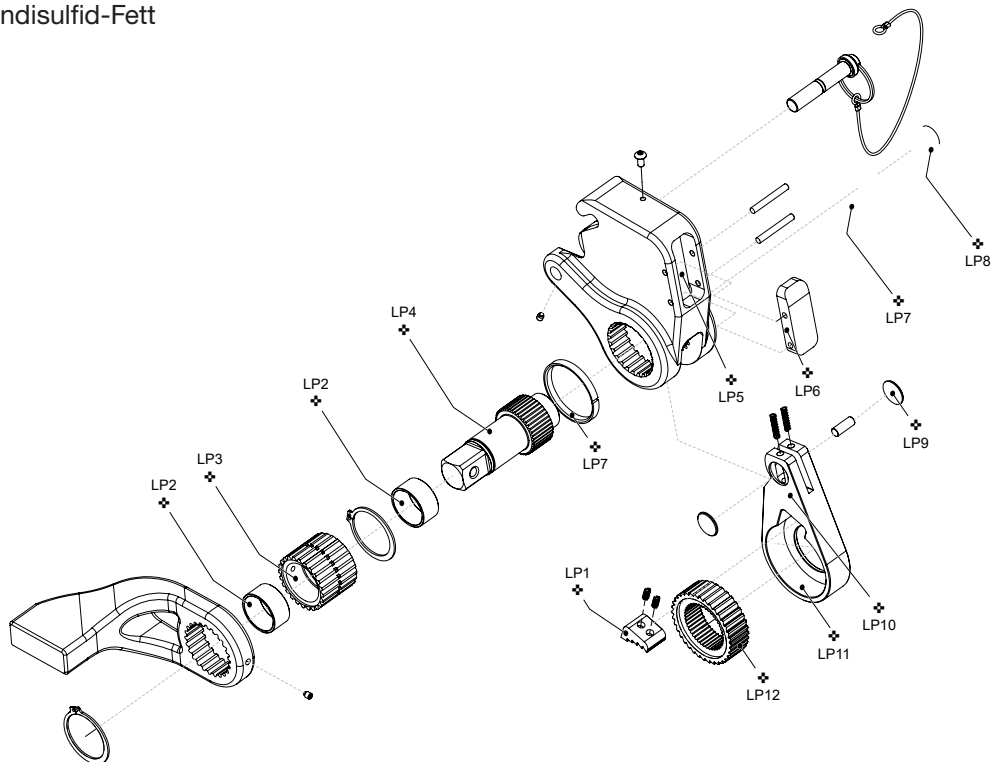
Explosionsansicht HMT HSQ-Kassette
